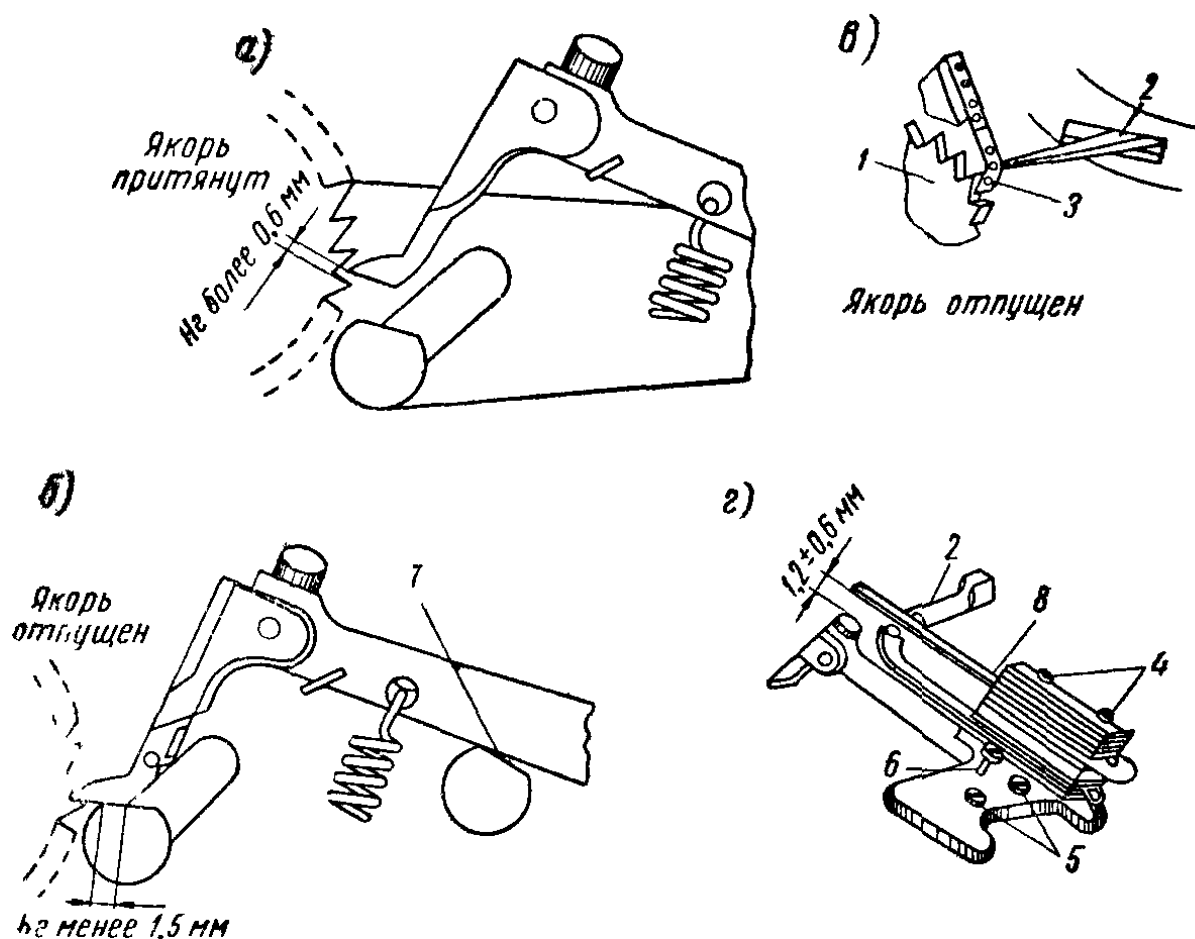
Регулировка собачек и самопрерывающегося контакта шагового искателя
